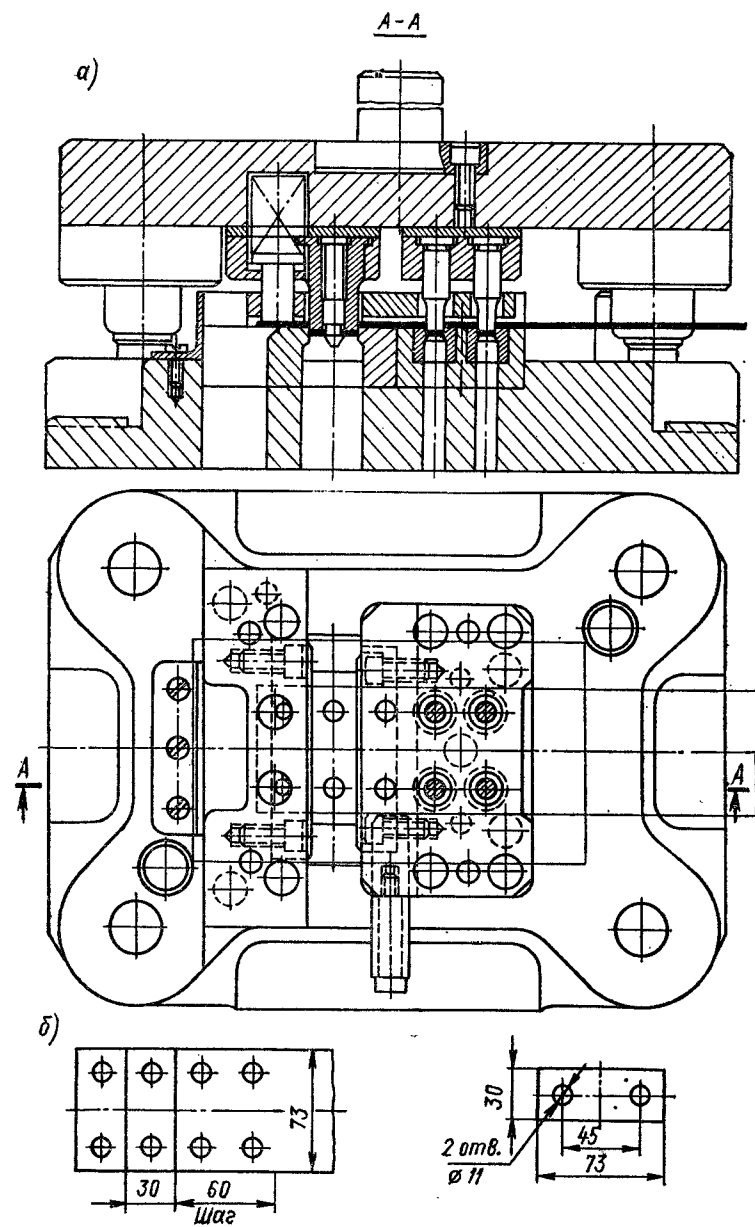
Последовательный штамп для пробивки и отрезки (по 2 шт. за рабочий ход)
